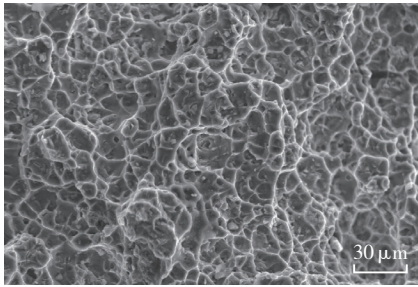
5A06-O铝合金UDP-VPTIG焊缝拉伸断口形貌
